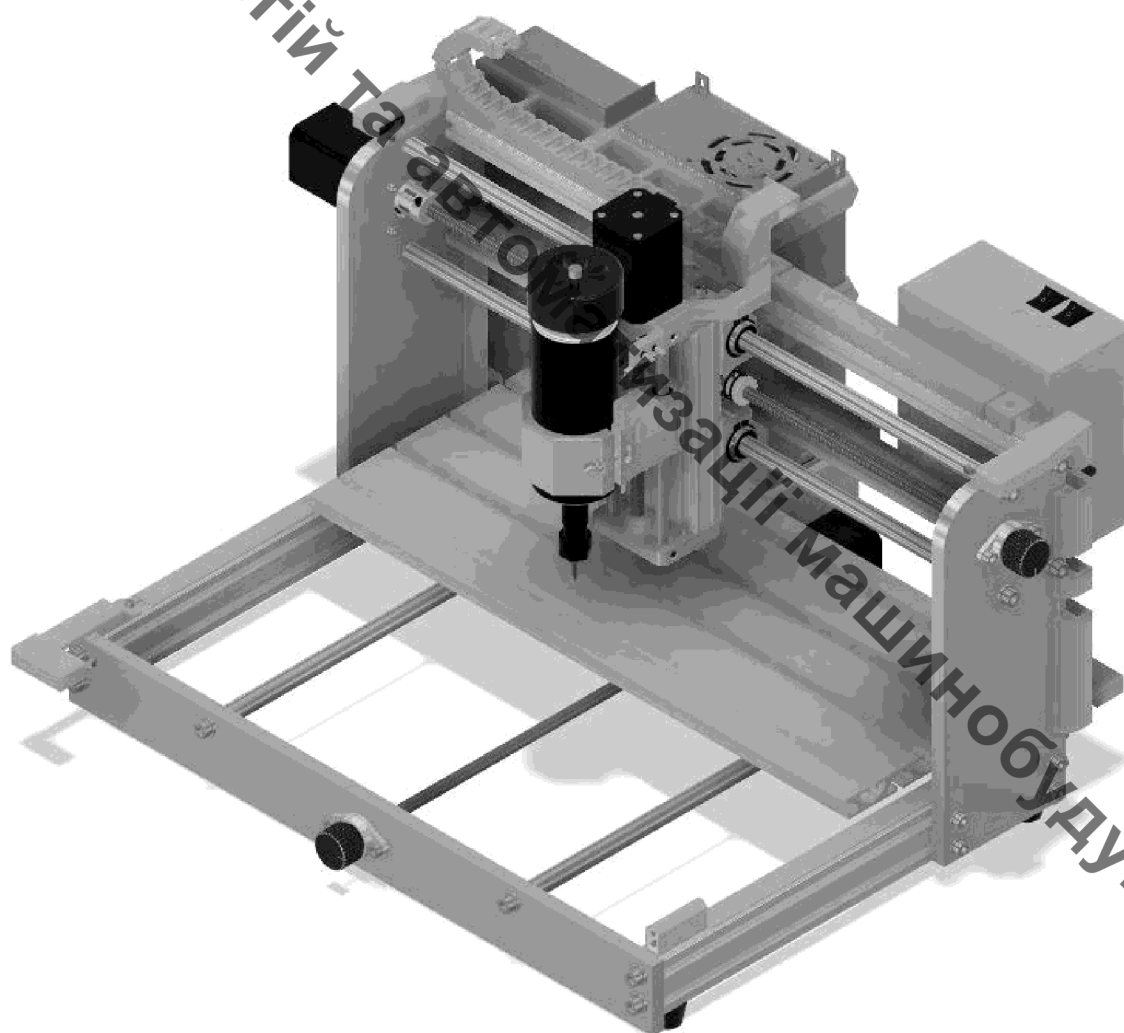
3-осьовий фрезерний верстат CNC 3018-Plus
